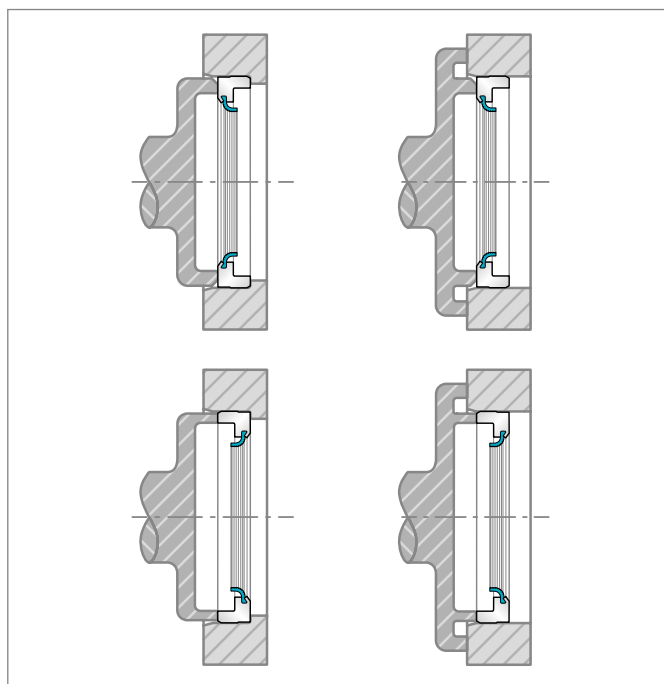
Montagewerkzeuge für das Einpressen in Gehäuse
